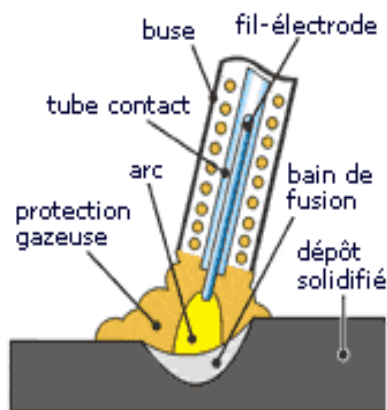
Schéma d'assemblage par soudage .
